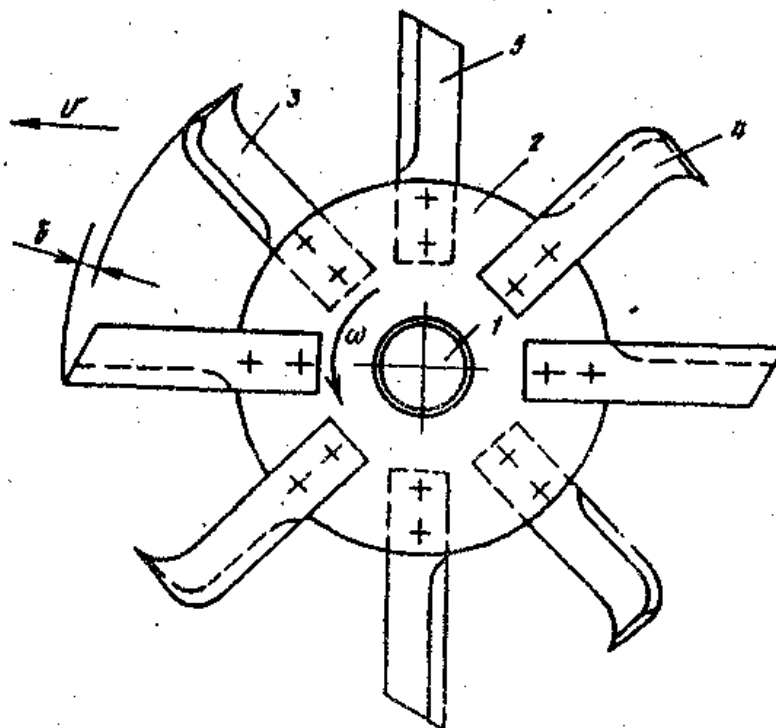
Принципова схема диска фрезерного барабана з ножами
